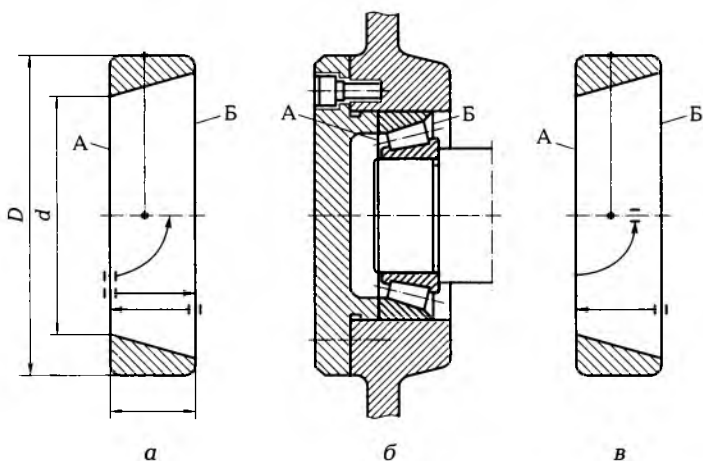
Схема роликоподшипника (а), требования к относительному положению поверхностей наружного кольца согласно рабочему чертежу (б) и в соответствии с его служебным назначением (в):
